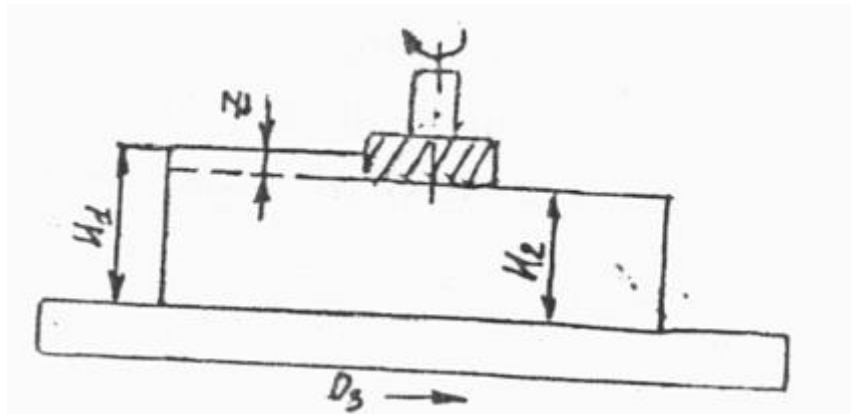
Связь размеров заготовки  $I_1$ , изделия  $I_2$  и припуска  $Z$
